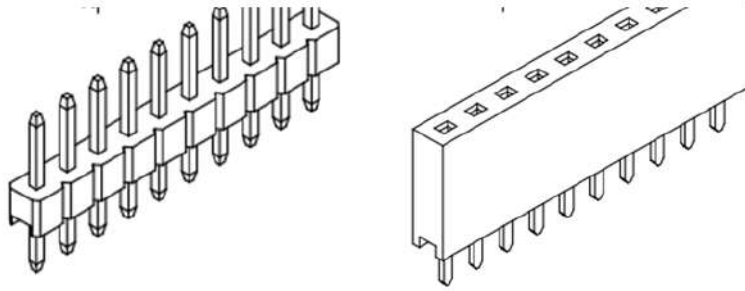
Роз’єми «2.00mm THT Straight Single Pin Header WR-PHD» та «WR-PHD Socket Header».[24]
